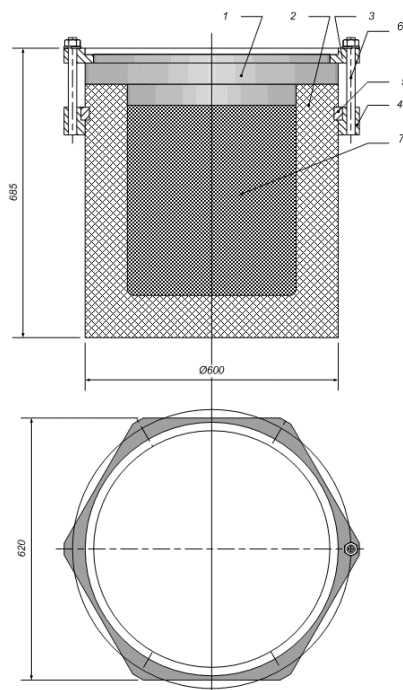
Сборочный чертеж контейнера-упаковки
